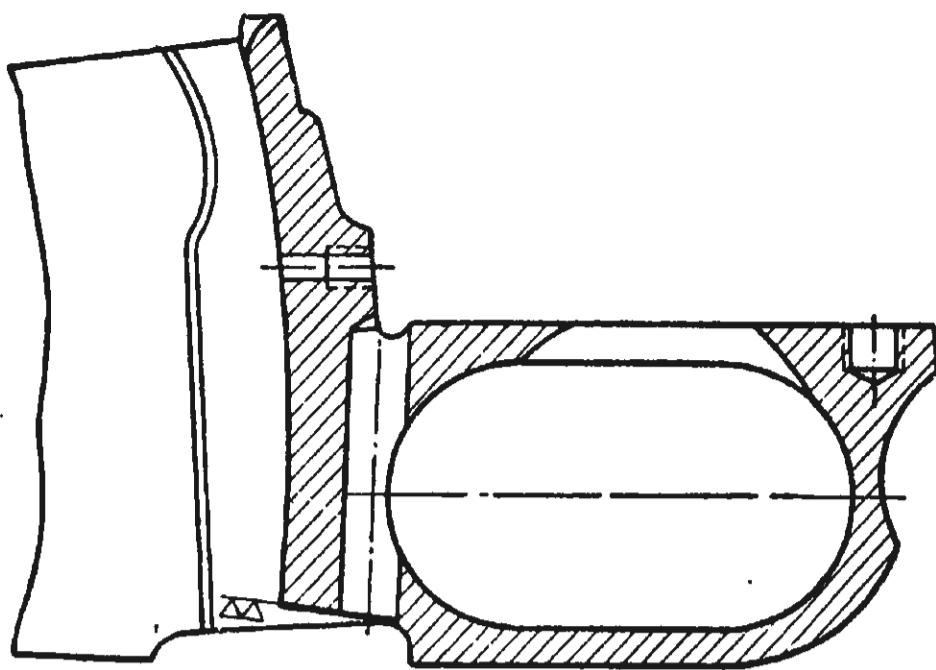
Зачистка площадки спусковой скобы магазинной коробки
